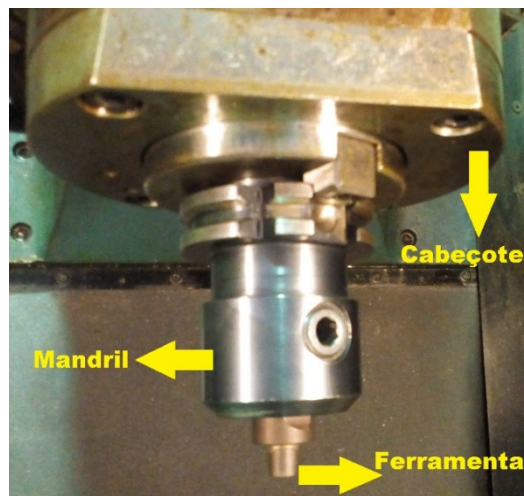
Cabeçote, mandril de fixação e ferramenta acoplados no centro de usinagem CNC Polaris V400, CEFCON COPPE/UFRJ.
